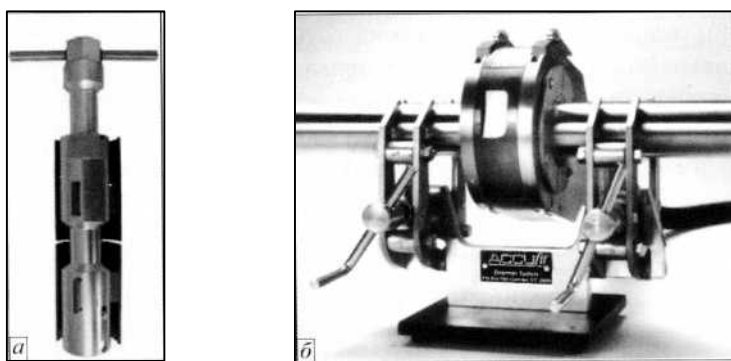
Центраторы для сборки труб (а — тип 1; б — тип 2)
